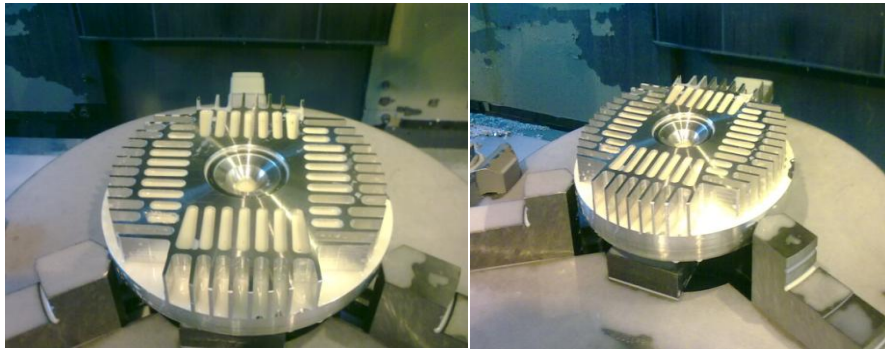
Frézování drážek a vybrání na spodní straně hlavy pomocí frézy průměru 6 mm do hloubky 22 mm
